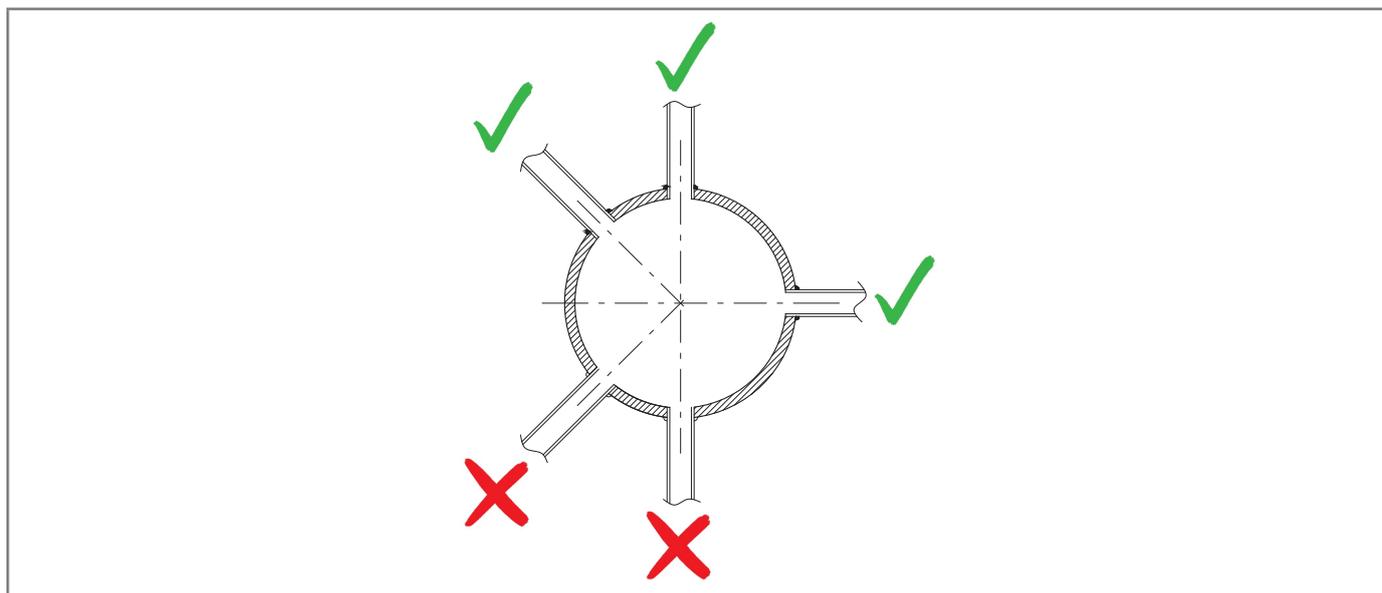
Raccords soudés de la connexion pneumatique
